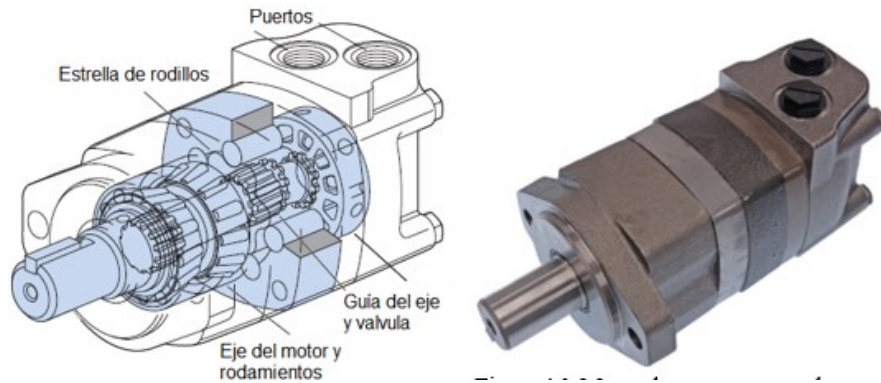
64. Motor de gerotor con paletas-rodillos.¹⁰⁹
